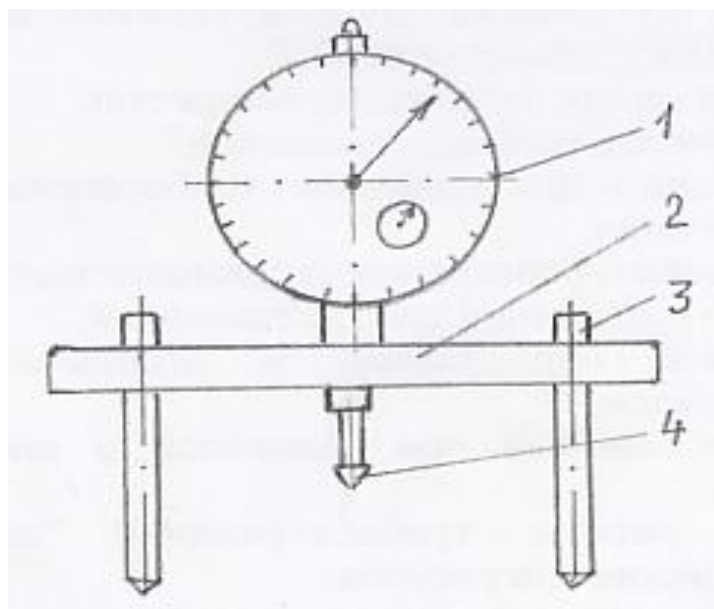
Вариант прибора для измерения диаметра поверхности круглых деталей больших диаметров по части дуги окружности: 1 – индикатор часового типа; 2 – планка; 3 – шпилька; 4 – наконечник ножки индикатора.
